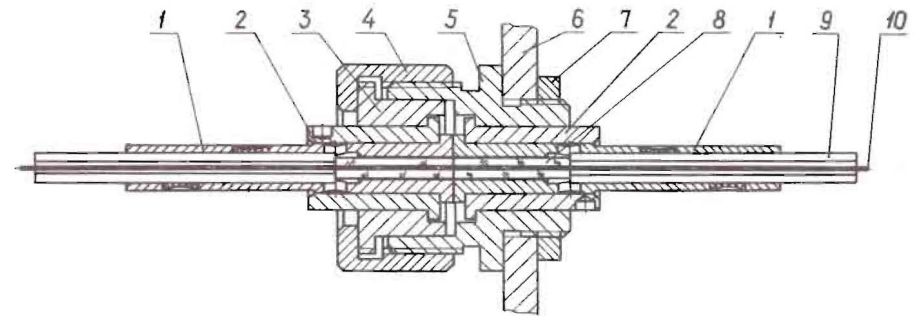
Юстируемый соединитель "световод-световод": 1 - втулка капилляра; 2 - втулка эксцентриковая; 3 - втулка фиксирующая; 4 - накидная гайка; 5 - корпус гильзы; 6 - панель прибора /при необходимости/; 7 - гайка; 8 - капилляр стеклянный; 9 - оболочка кабеля; 10 - световод.
